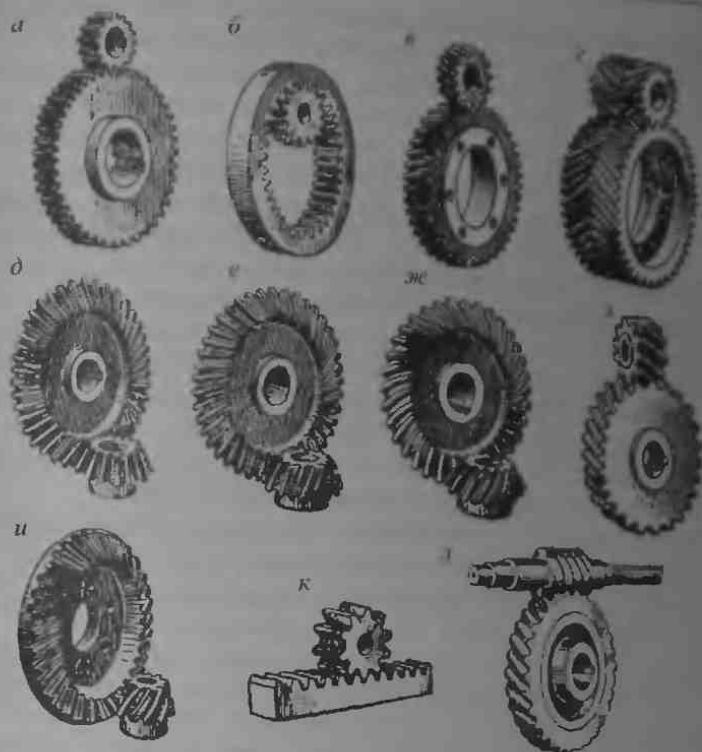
Типы зубчатых передач: а) прямозубая с внешним зацеплением; б) прямозубая с внутренним зацеплением; в) косозубая цилиндрическая; г) шевронная; д) коническая прямозубая; е) коническая косозубая; ж) коническая с криволинейными зубьями; з) винтовая; и) гипоидная; к) реечная; л) червячная
